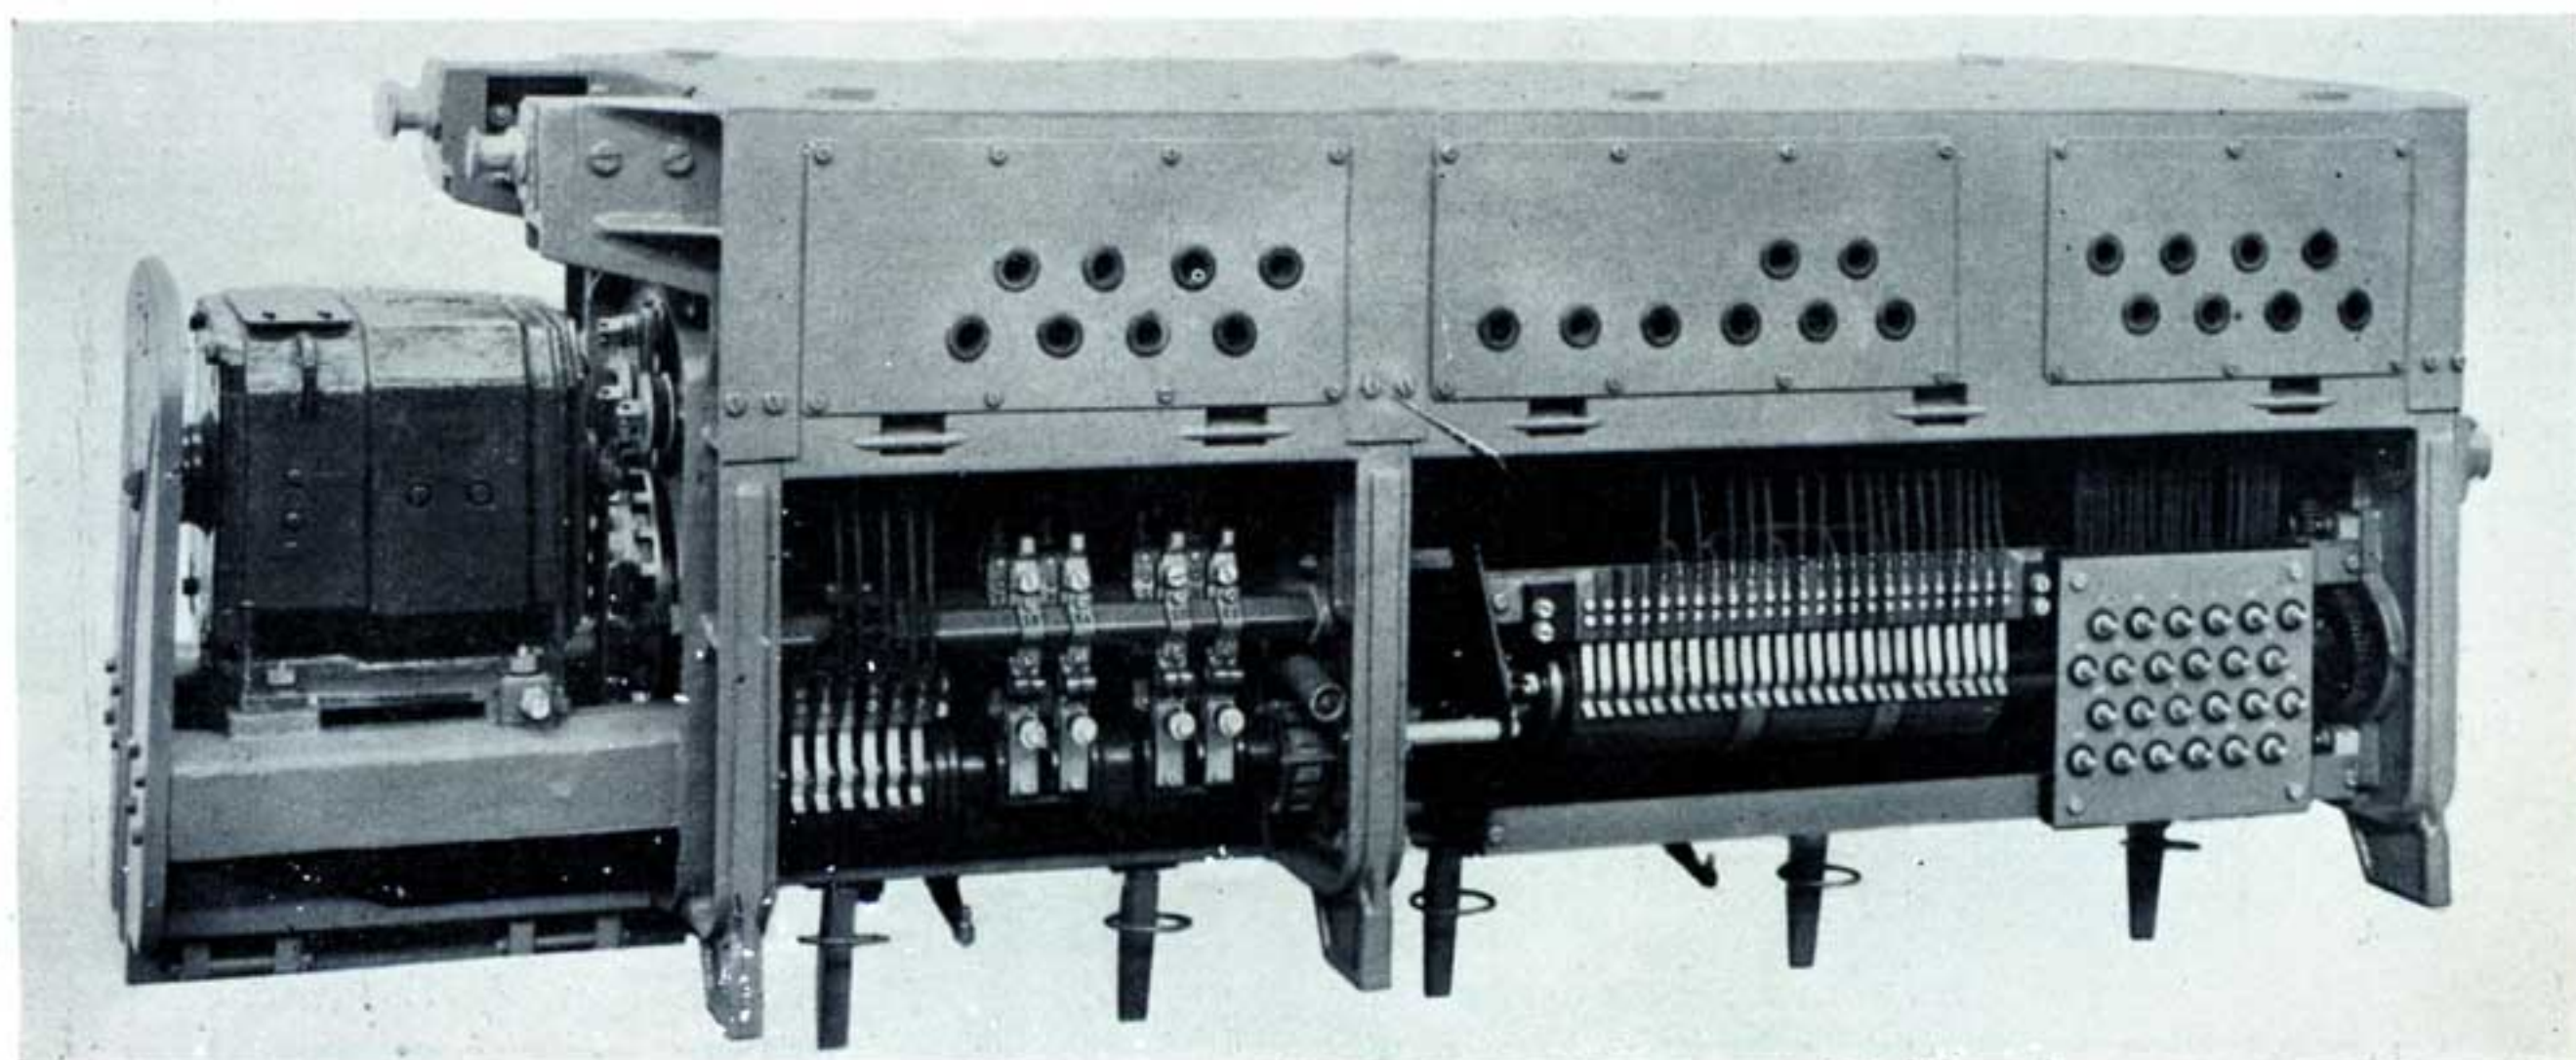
Coffre JH ouvert. Vue côté arrière.
